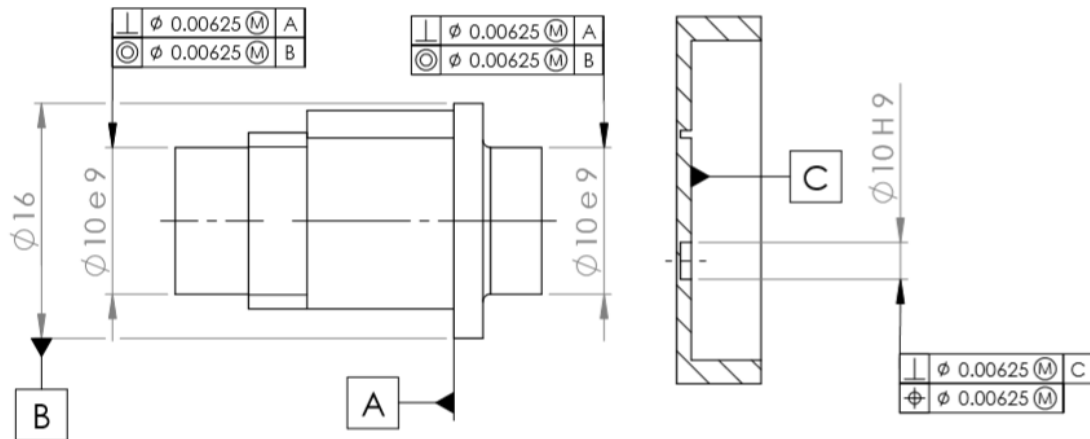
Representación de las tolerancias geométricas de perpendicularidad y sus referencias para la parte izquierda del eje y la tapa izquierda.
